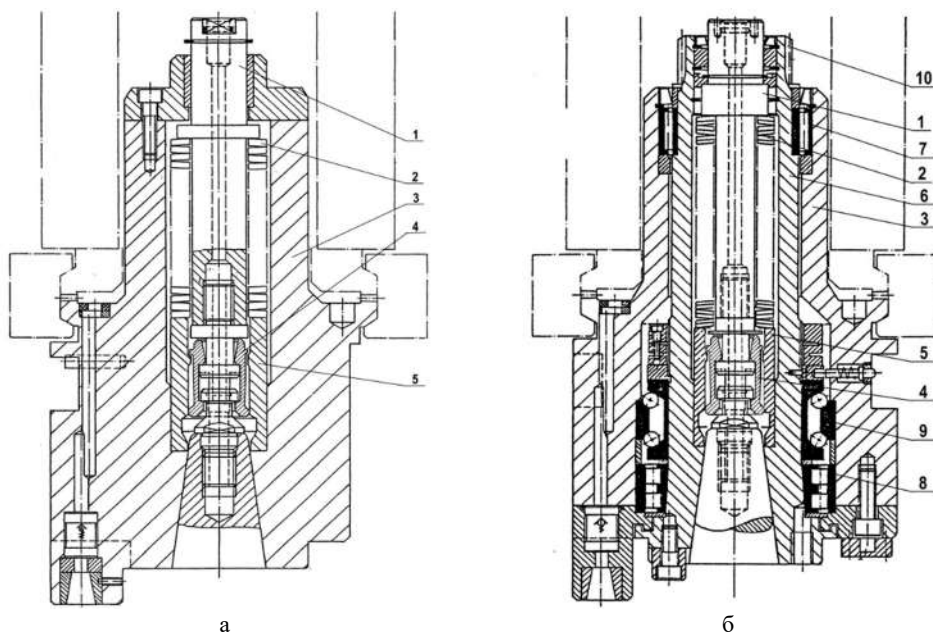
Інструментальні головки верстата: а – токарний адаптер; б – фрезерно-розточувальна головка
